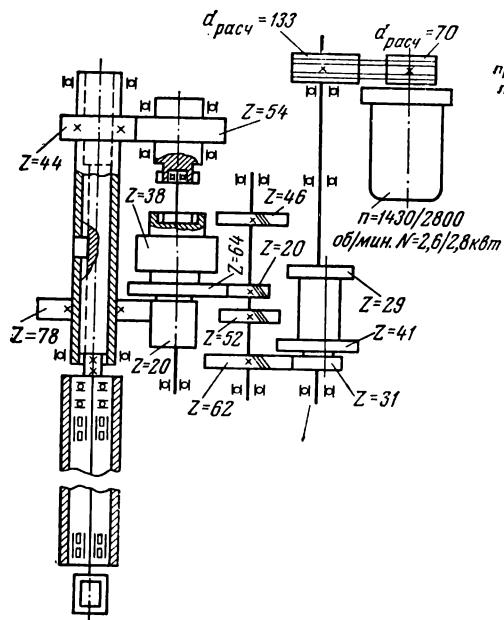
Кинематическая схема привода главного движения станка модели ЛР-87
